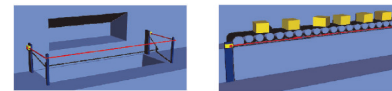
Förderbänder, Bearbeitungszentren, Verpackungsmaschinen...
